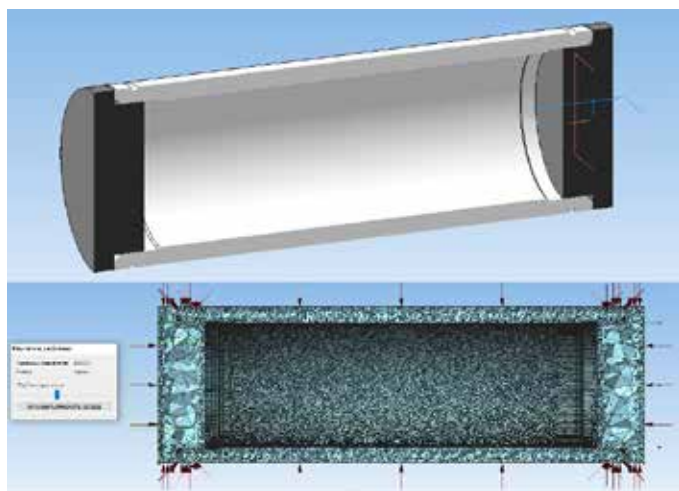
Корпус в сборе. Разбивка корпуса на конечные элементы – тетраэдры.
